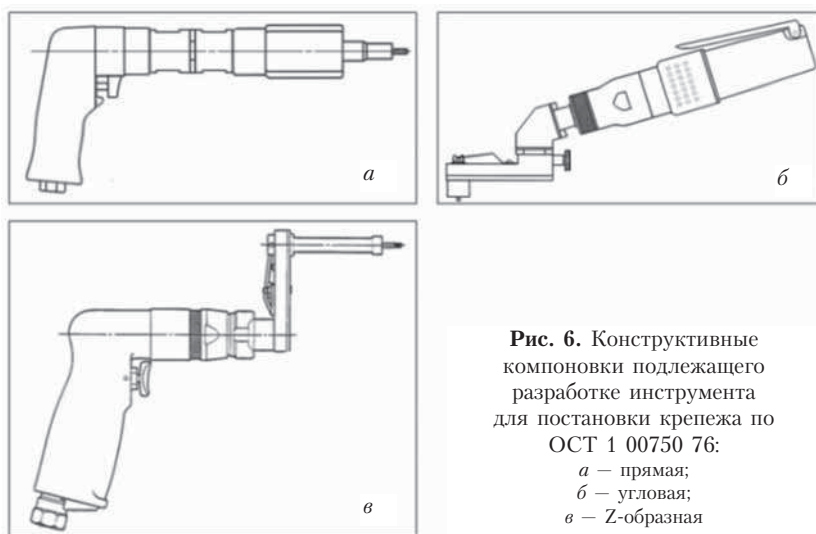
Конструктивные компоновки подлежащего разработке инструмента для постановки крепежа по ОСТ 1 00750 76:
